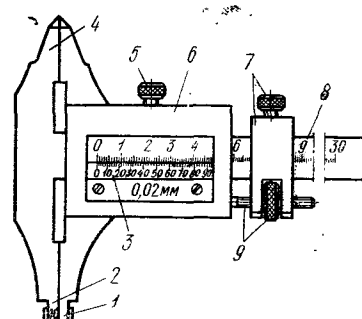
Устройство штангенциркуля с ценой деления 0,02 мм
